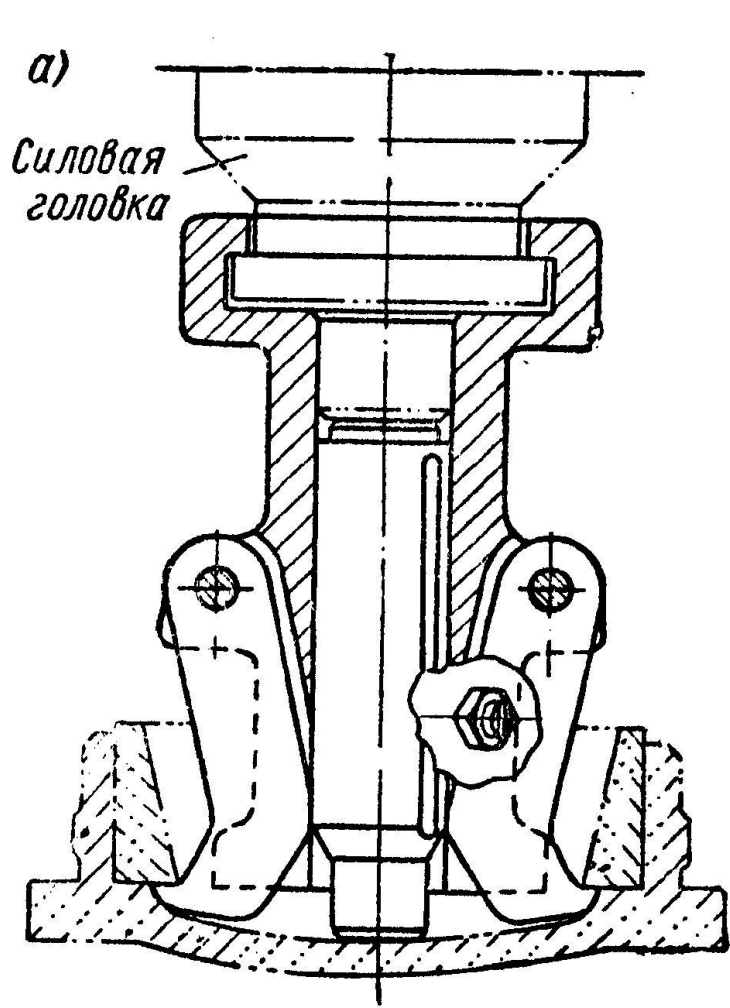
Съемник для выдрессовки гильз из блока цилиндров двигателя ЗИЛ-130
